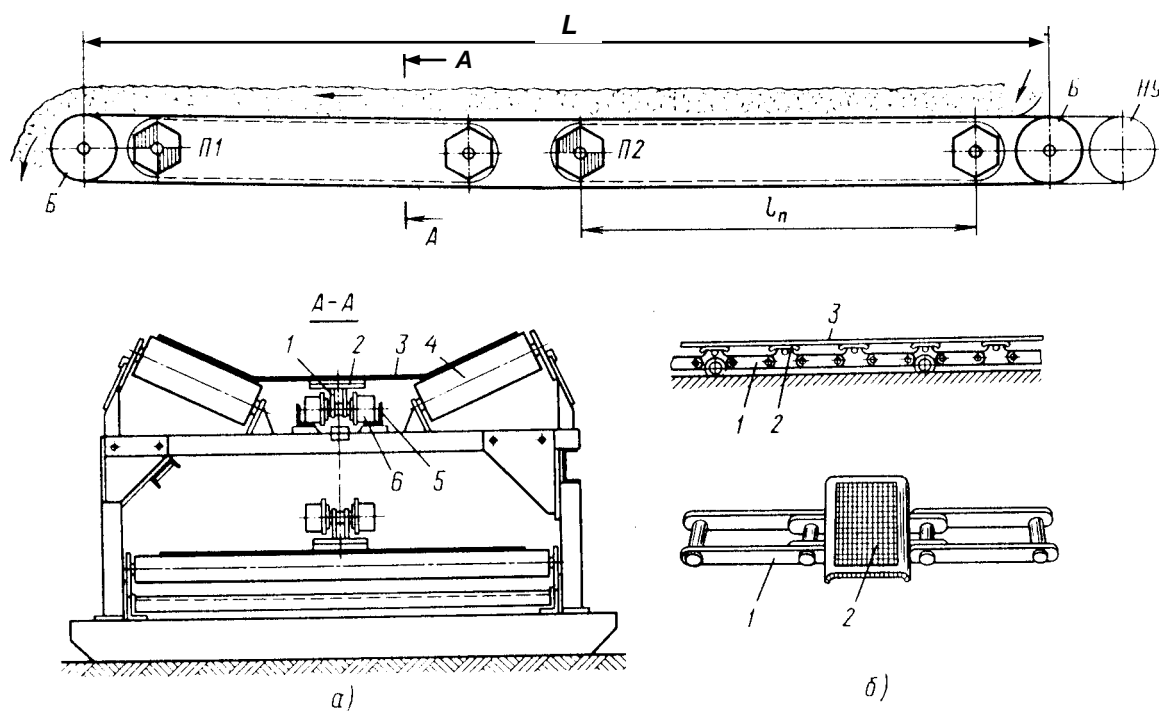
Ленточно-цепной конвейер: а) схема; б) – ходовая часть; Б – оборотный барабан; П1, П2 - приводные звездочки; НУ - натяжное устройство
